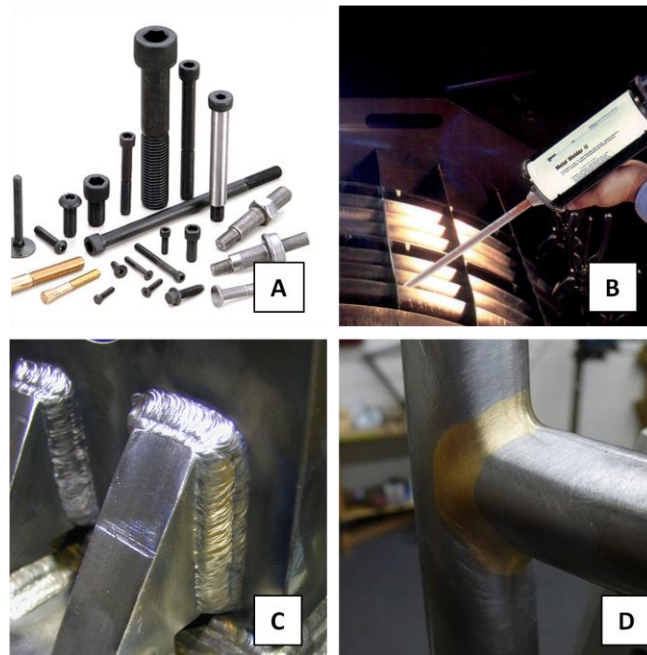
Ejemplos de los cuatro principales procesos de unión utilizados en la “Industria Ligera”: A) Fijación Mecánica; B) Adhesivos; C) Soldadura por Fusión; D) Soldadura mediante Capilaridad [13].
